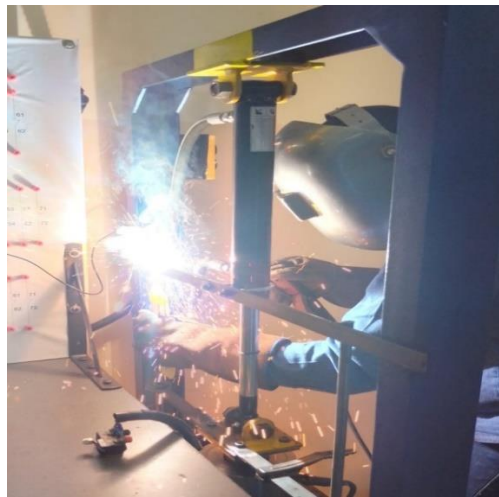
Soldadura de los ejes de los bocines para la guía del pistón hidráulico
